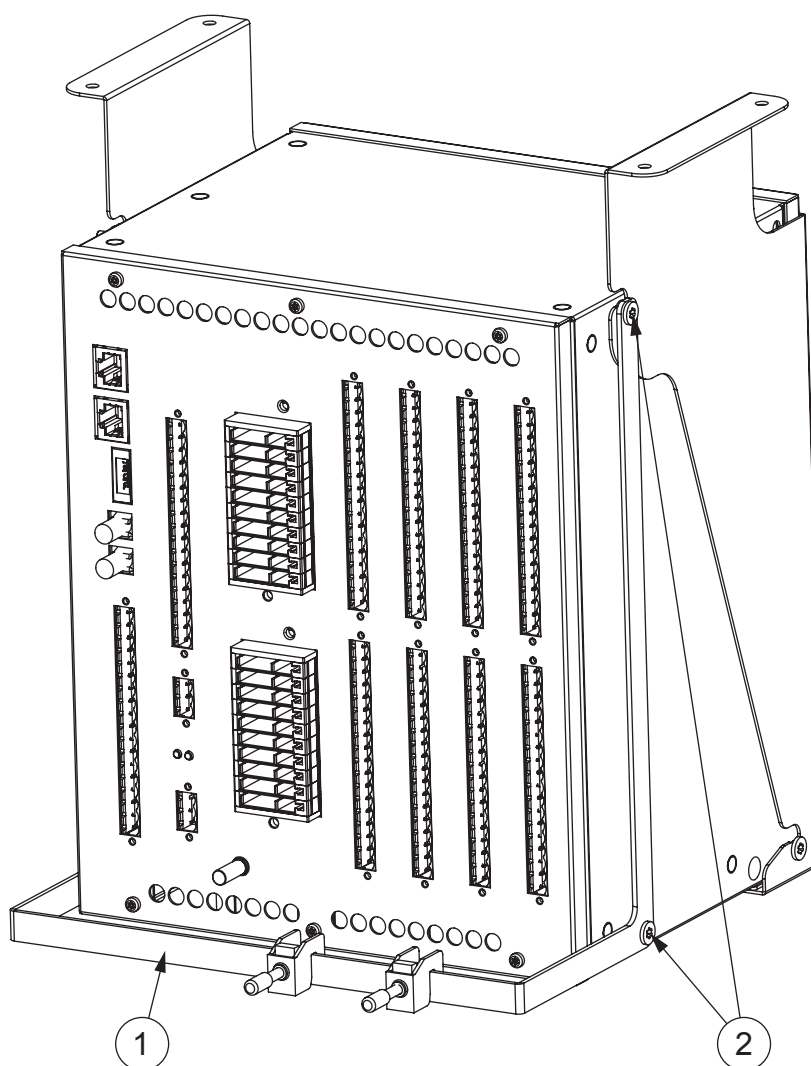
Media 19" 6U Montaje del raíl de sujeción del cable opcional
